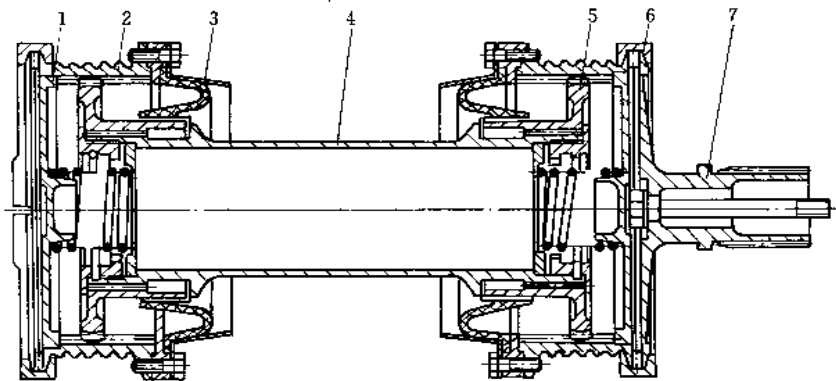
机车万向联轴器传动轴用来连接牵引发机电枢轴与起动变速箱主动轴。在十字头各轴颈上，分别装上橡胶密封圈轴套，再将其装入轴承体内。十字头组装后，安装在法兰或法兰与叉头轴的半圆孔中，再用两个 M12 螺栓把轴承盖压紧固定在法兰、叉头轴或叉头上。轴承体与其相接合件之间均为过渡配合，而轴承套、轴承体及轴颈之间均为间隙配合。
